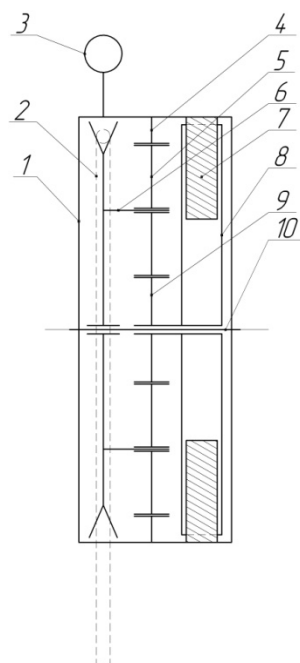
Устройство спасательное: 1 – корпус; 2 – спасательная веревка; 3 – верхний подвес; 4 – эпициклическая шестерня; 5 – сателлит; 6 – водило (шкив); 7 – груз центробежного тормоза; 8 – ведущий элемент центробежного тормоза; 9 – солнечная шестерня; 10 – ось
